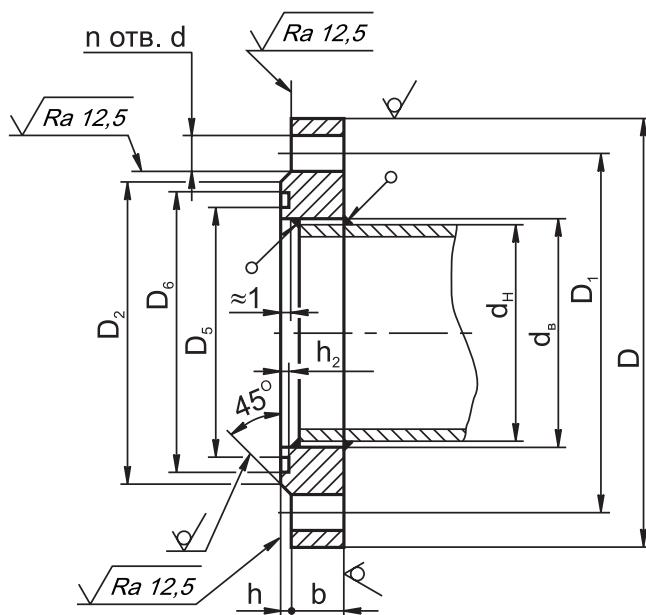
Размеры ответных фланцев для фильтров с присоединительными фланцами PN 16
